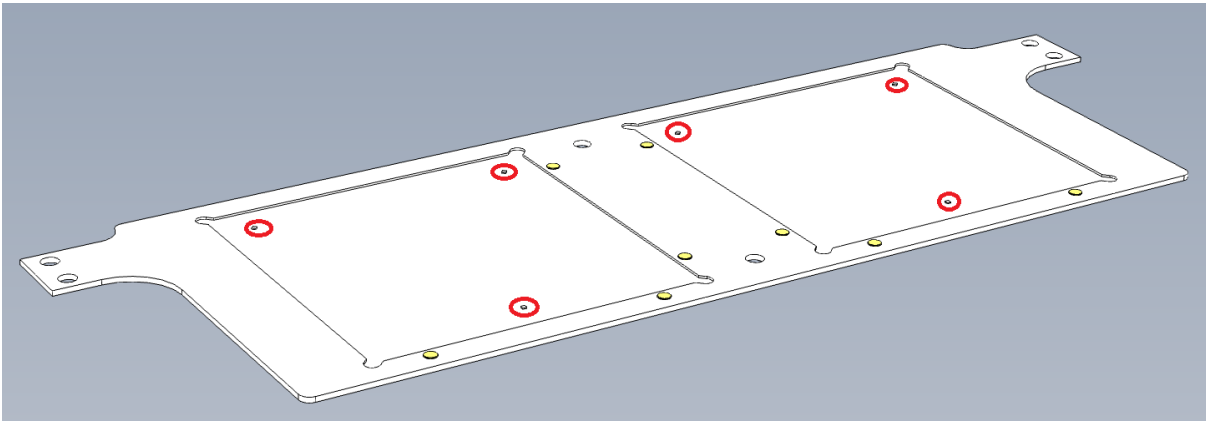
neu entwickelte Bootplatte für ein kleines Horizontalboot aufgrund neuester Erkenntnisse. Hinzugekommen sind die gelben Haltepins für Masken. Die rot markierten Auflagepins für Wafer wurden im Zuge der weiteren Optimierung entfernt.
